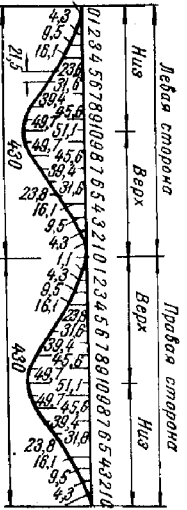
Разметка конца отрезка сварного тройника.
